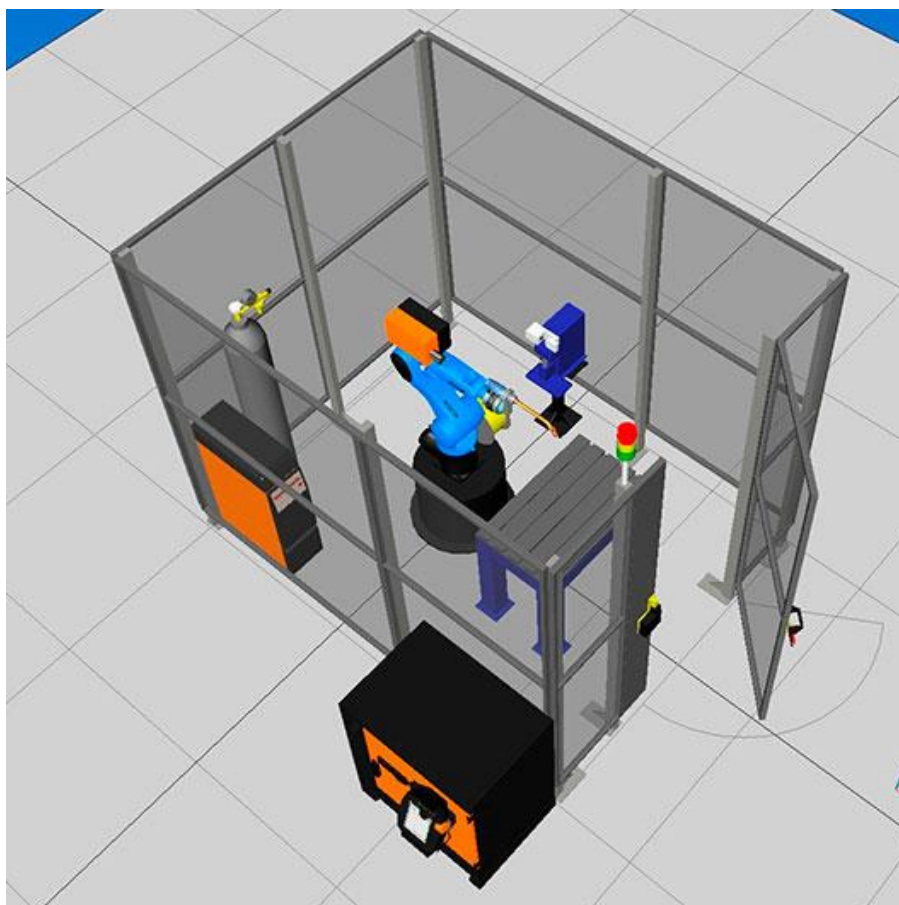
Сварочный робот KUKA / Сварочная машина Fronius.
